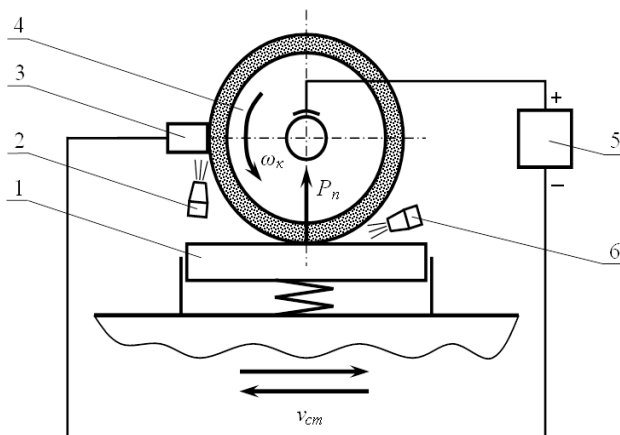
Схема плоского урізного шліфування за пружною схемою з постійною силою притискання  $P_n$  оброблюваного зразка до робочій поверхні круга
